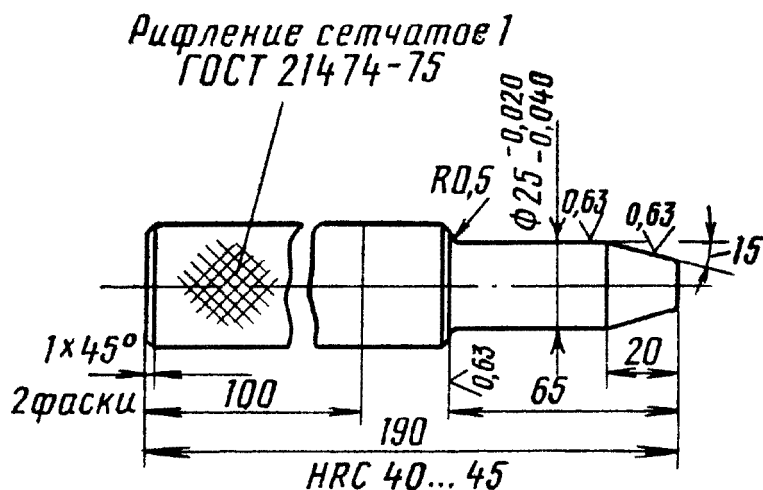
Оправка для установки штоков в корпус крышки коробки передач
